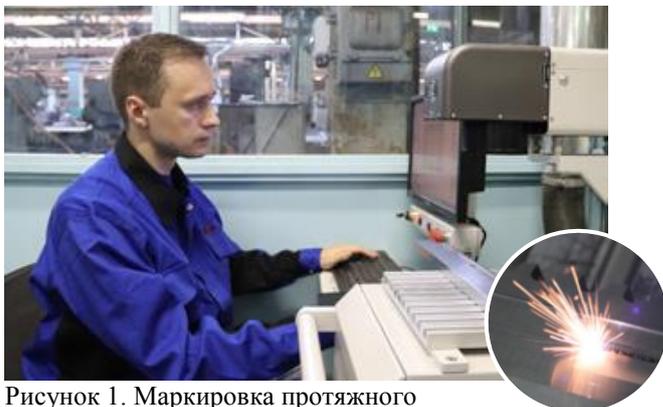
Маркировка протяжного инструмента: лазерный станок (слева) и процесс нанесения штрихового кода
